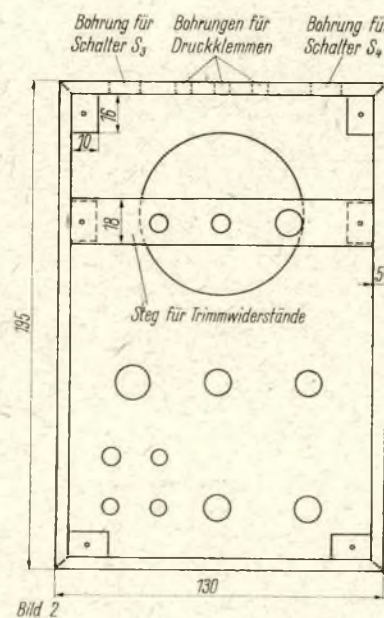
Maßskizze für das Gehäuse des Transistormeßgerätes (Ansicht von der Rückseite)
